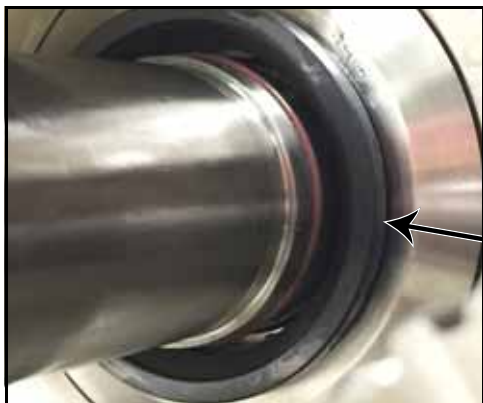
Zakładanie o-ringu łączącego uchwyt z uszczelką
